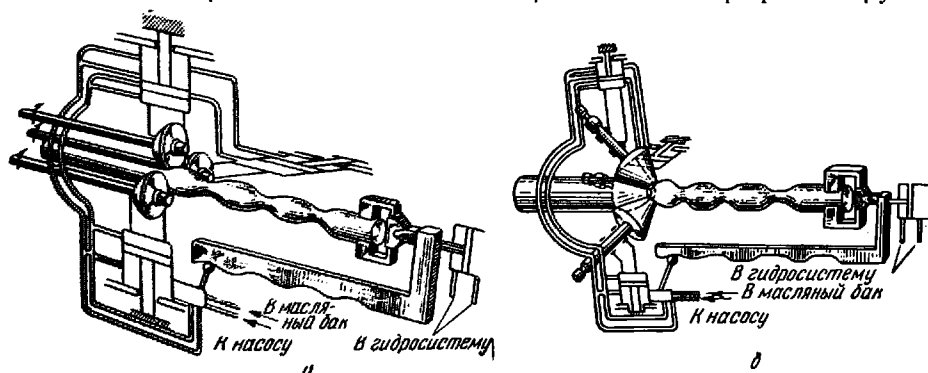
Схема прокатки на трехвалковых станах с валками: а — дисковыми; б — коническими
